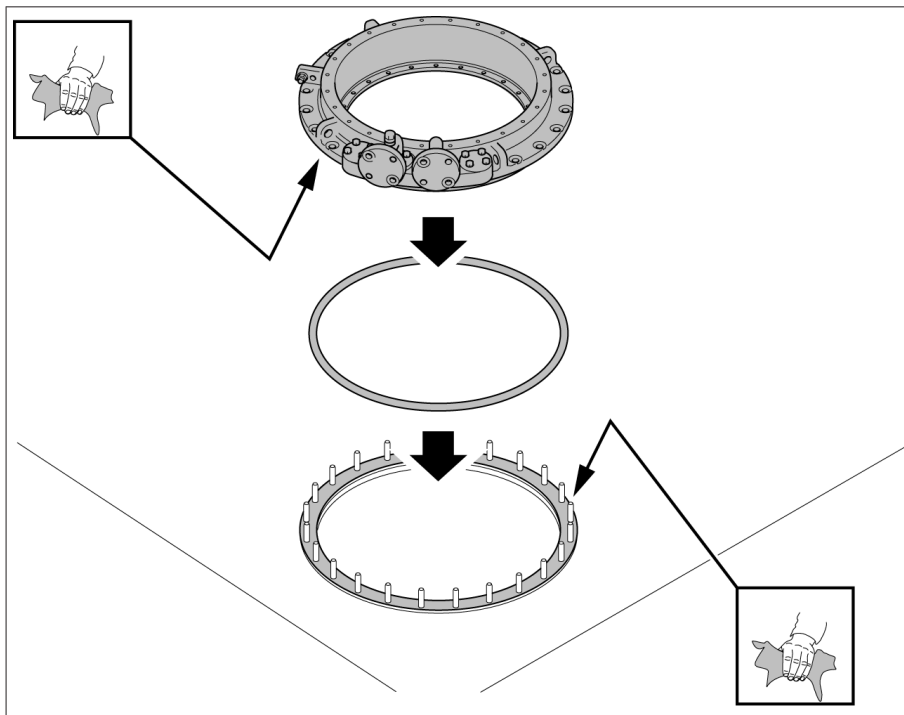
Aufbauflansch und Laststufenschalterkopf
